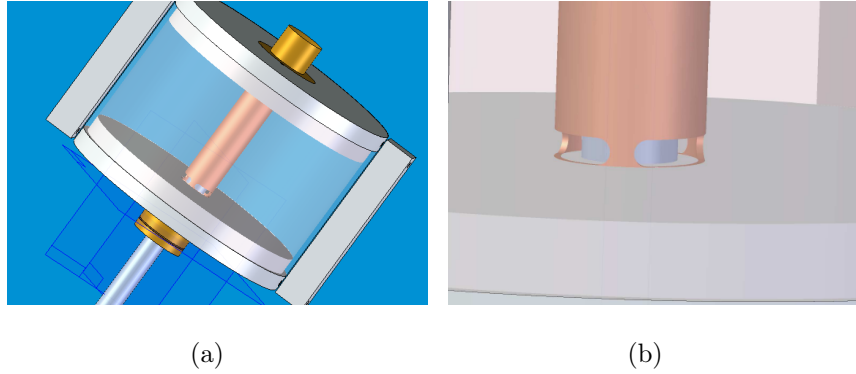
Detalle del sistema de centrado y de las entradas al conducto anular.
